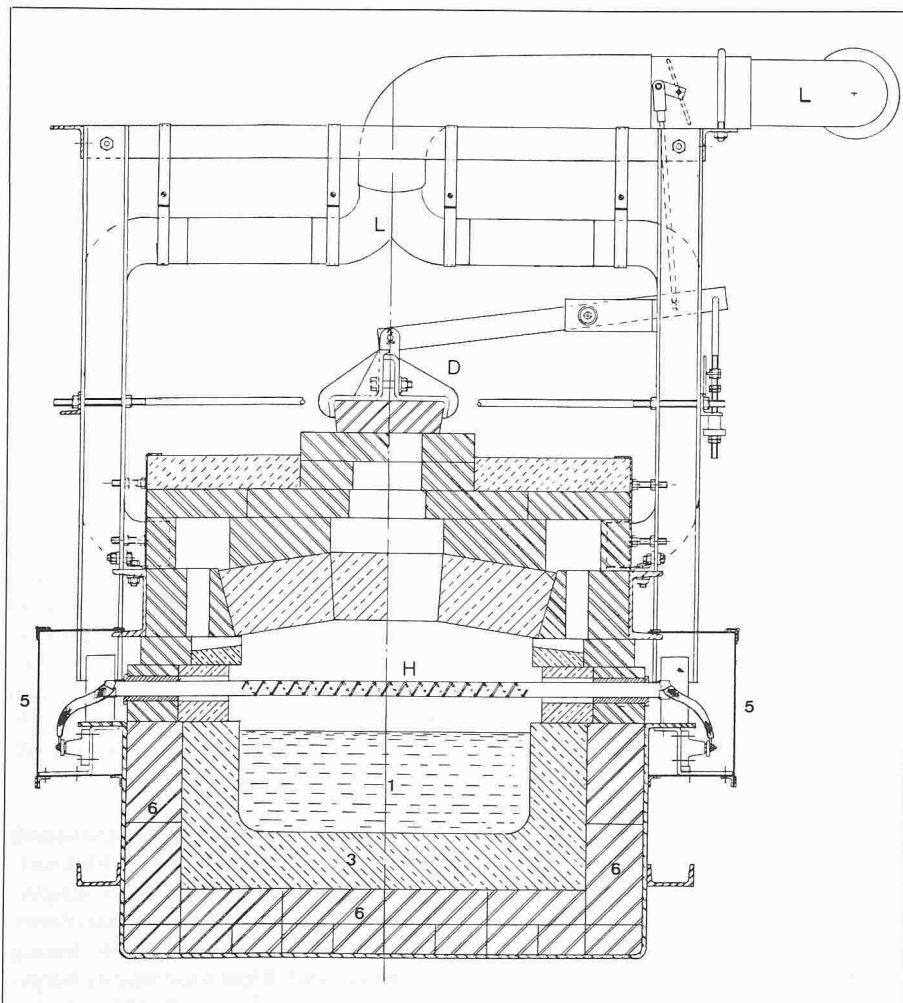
Schnitt durch die Kühlzone eines elektrisch beheizten Feeder-Vorherdes moderner Ausführung.
